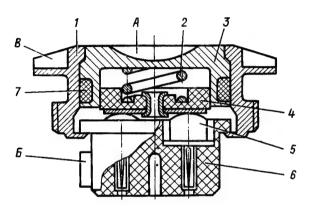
Переключатель: I — заглушка; 2 — пружина; 3 — вкладыш; 4 — ползун; 5 — контакт; 6 — розет-ка; 7 — кольцо; A, B — шлицы; B — ключ
